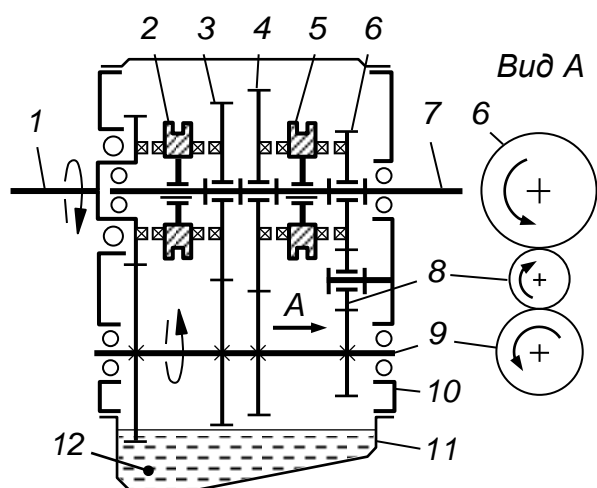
Кинематическая схема механической трёхступенчатой коробки передач:
